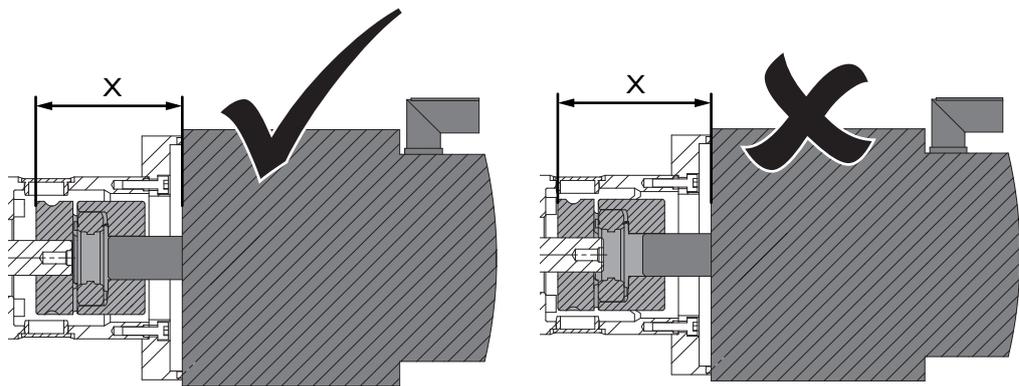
Posicionar el acoplamiento en el eje del motor: aprovechar la medida de tolerancia X
